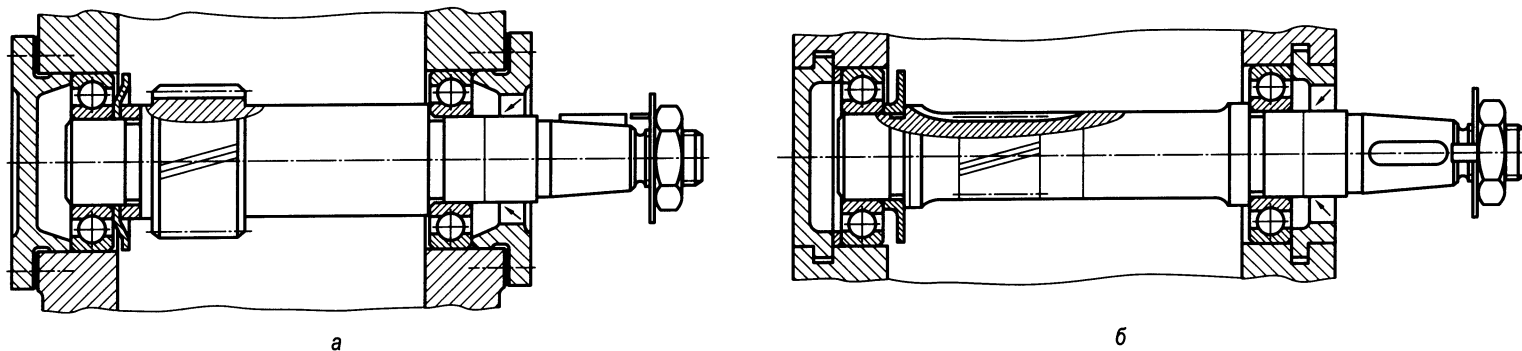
Вал-шестерня цилиндрического зубчатого редуктора (а – исполнение со свободным входом зубонарезного инструмента; б – врезная шестерня)
